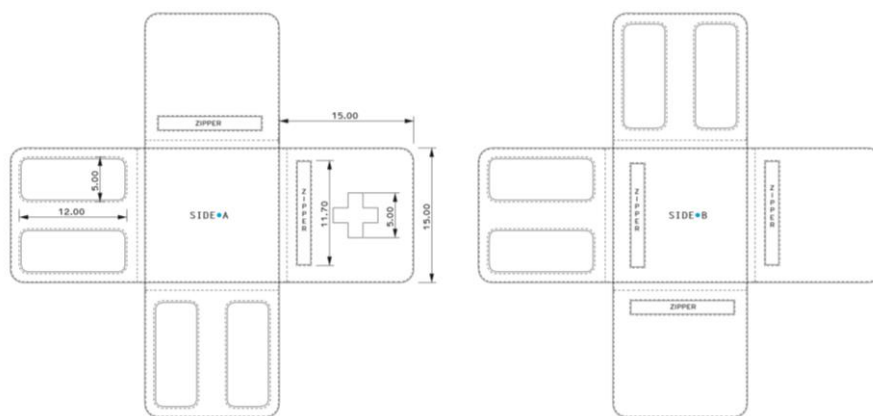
Desenho Técnico da Braçadeira. (Fonte: Dossier de Projeto cedido pelo autor).
